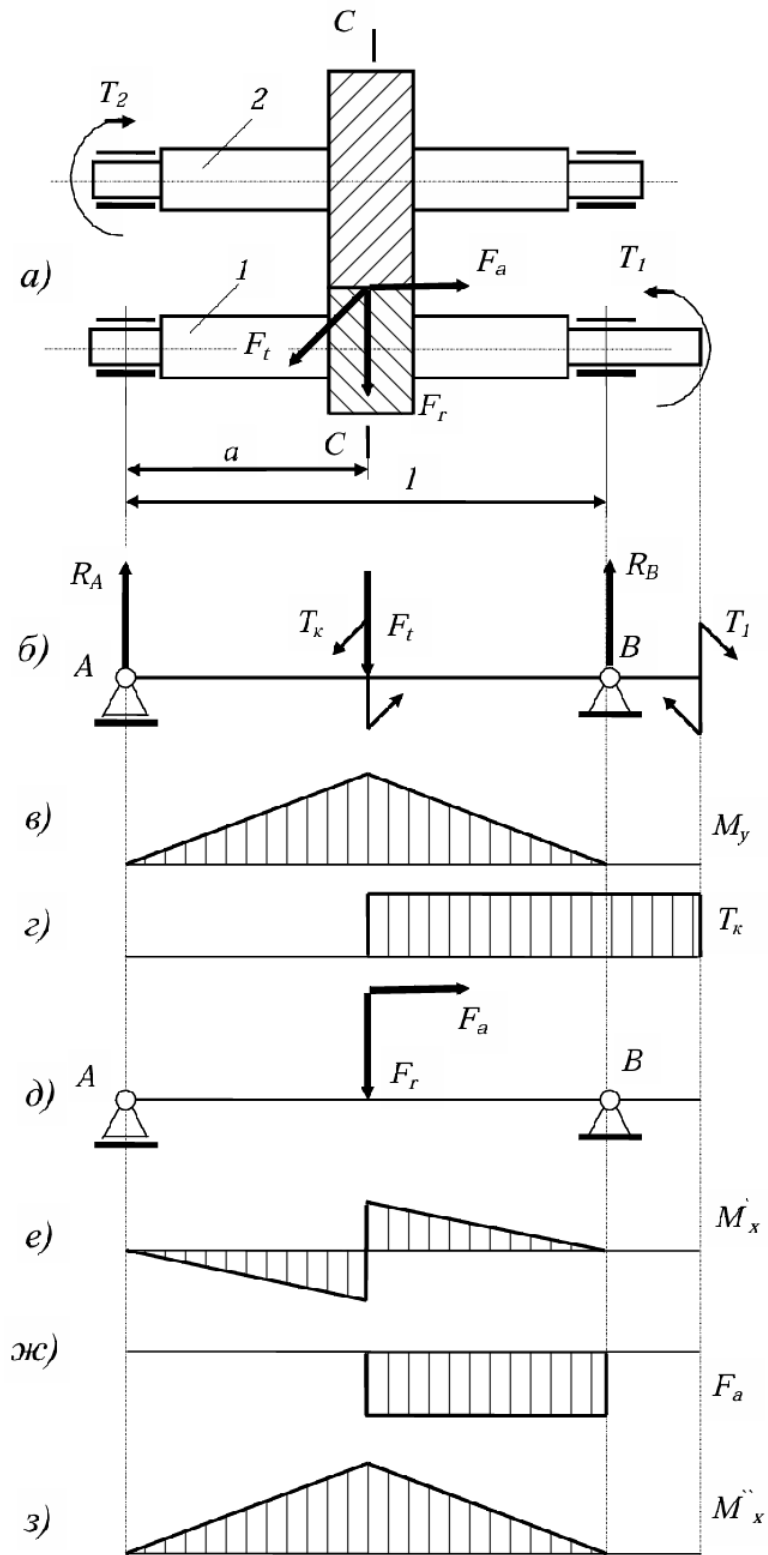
Расчетные схемы вала зубчатой передачи
